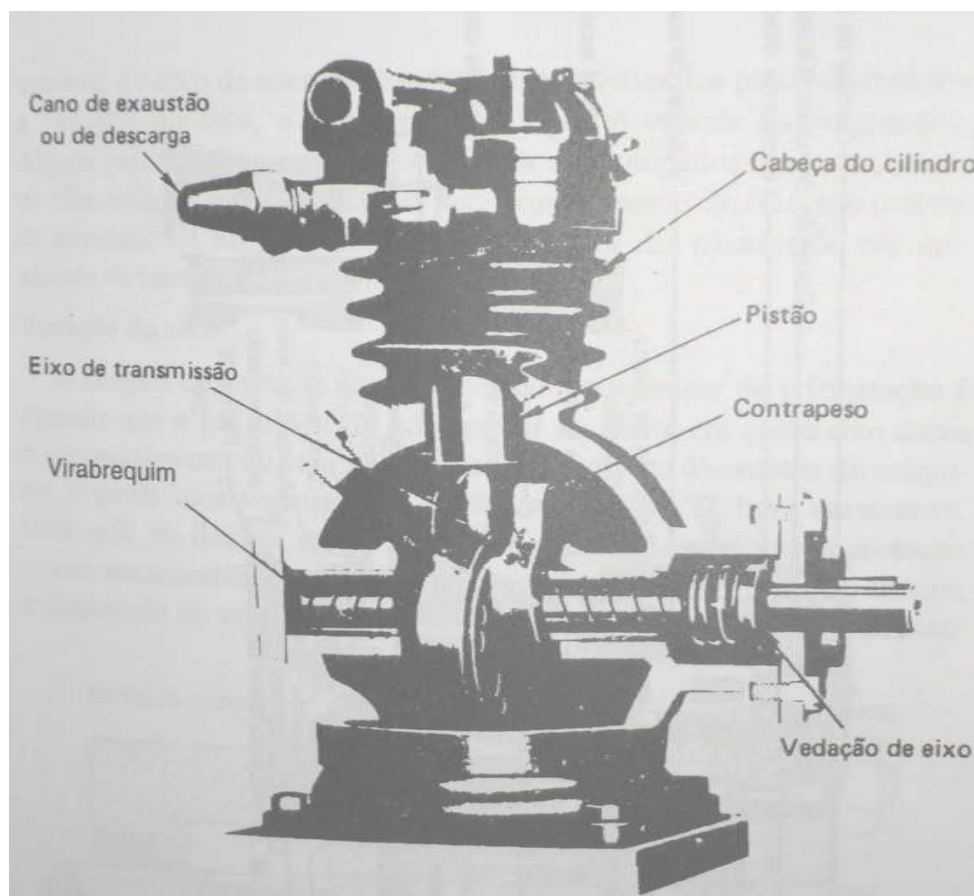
Vista de corte de um compressor de refrigeração alternado movido a correia, com um único cilindro.
